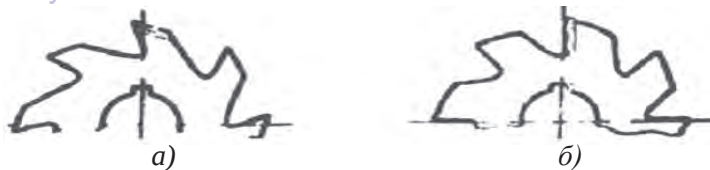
Виды фрез: а – с острозаточенными зубьями; б – фрез для шлифовки.
